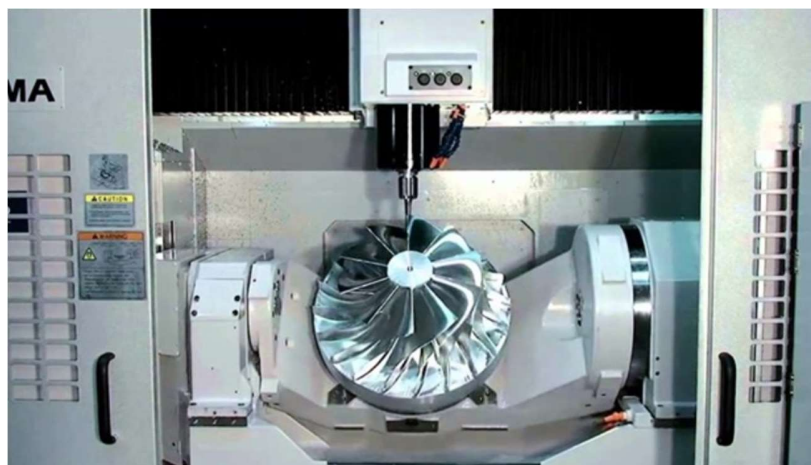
Високошвидкісна обробка металу на п'ятиосьовому фрезерному верстаті з ЧПУ
